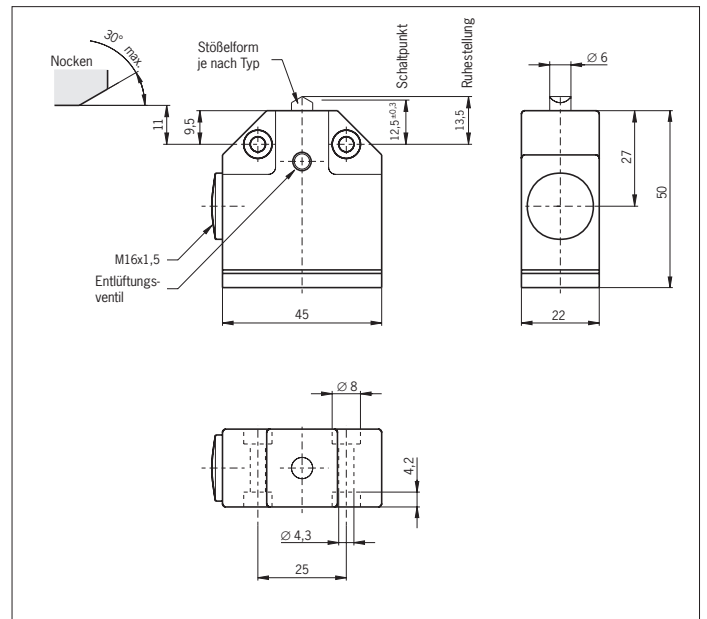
Maßzeichnung SN01... mit Leitungseinführung
